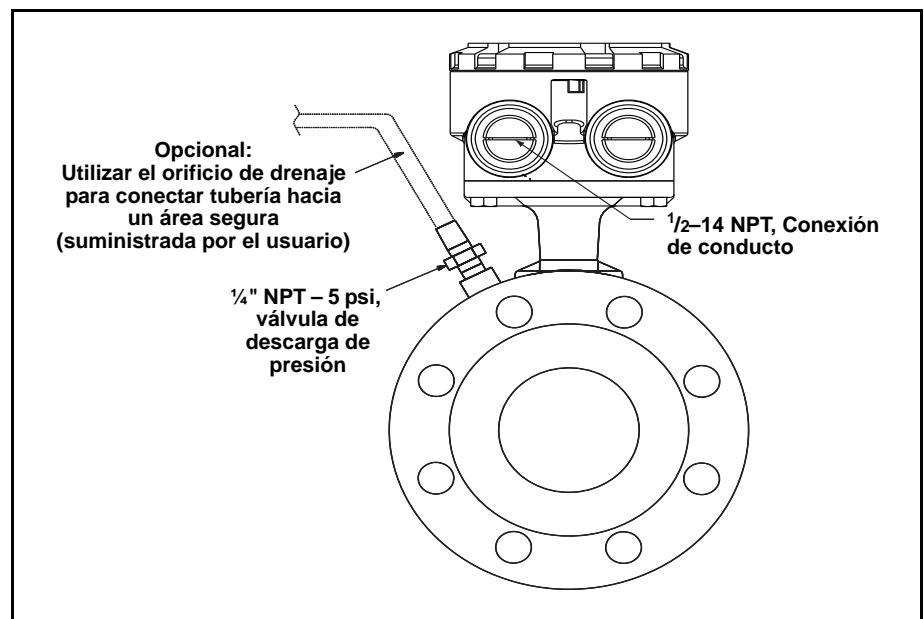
Configuración estándar de la carcasa – carcasa sellada y soldada (código de opción W0)
